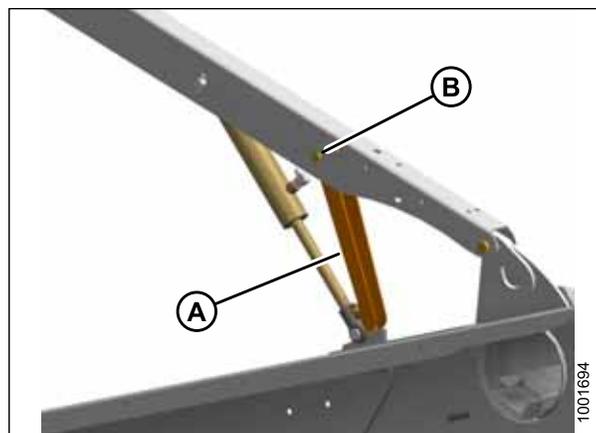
Предохранительный упор мотовила — левый внешний рычаг
